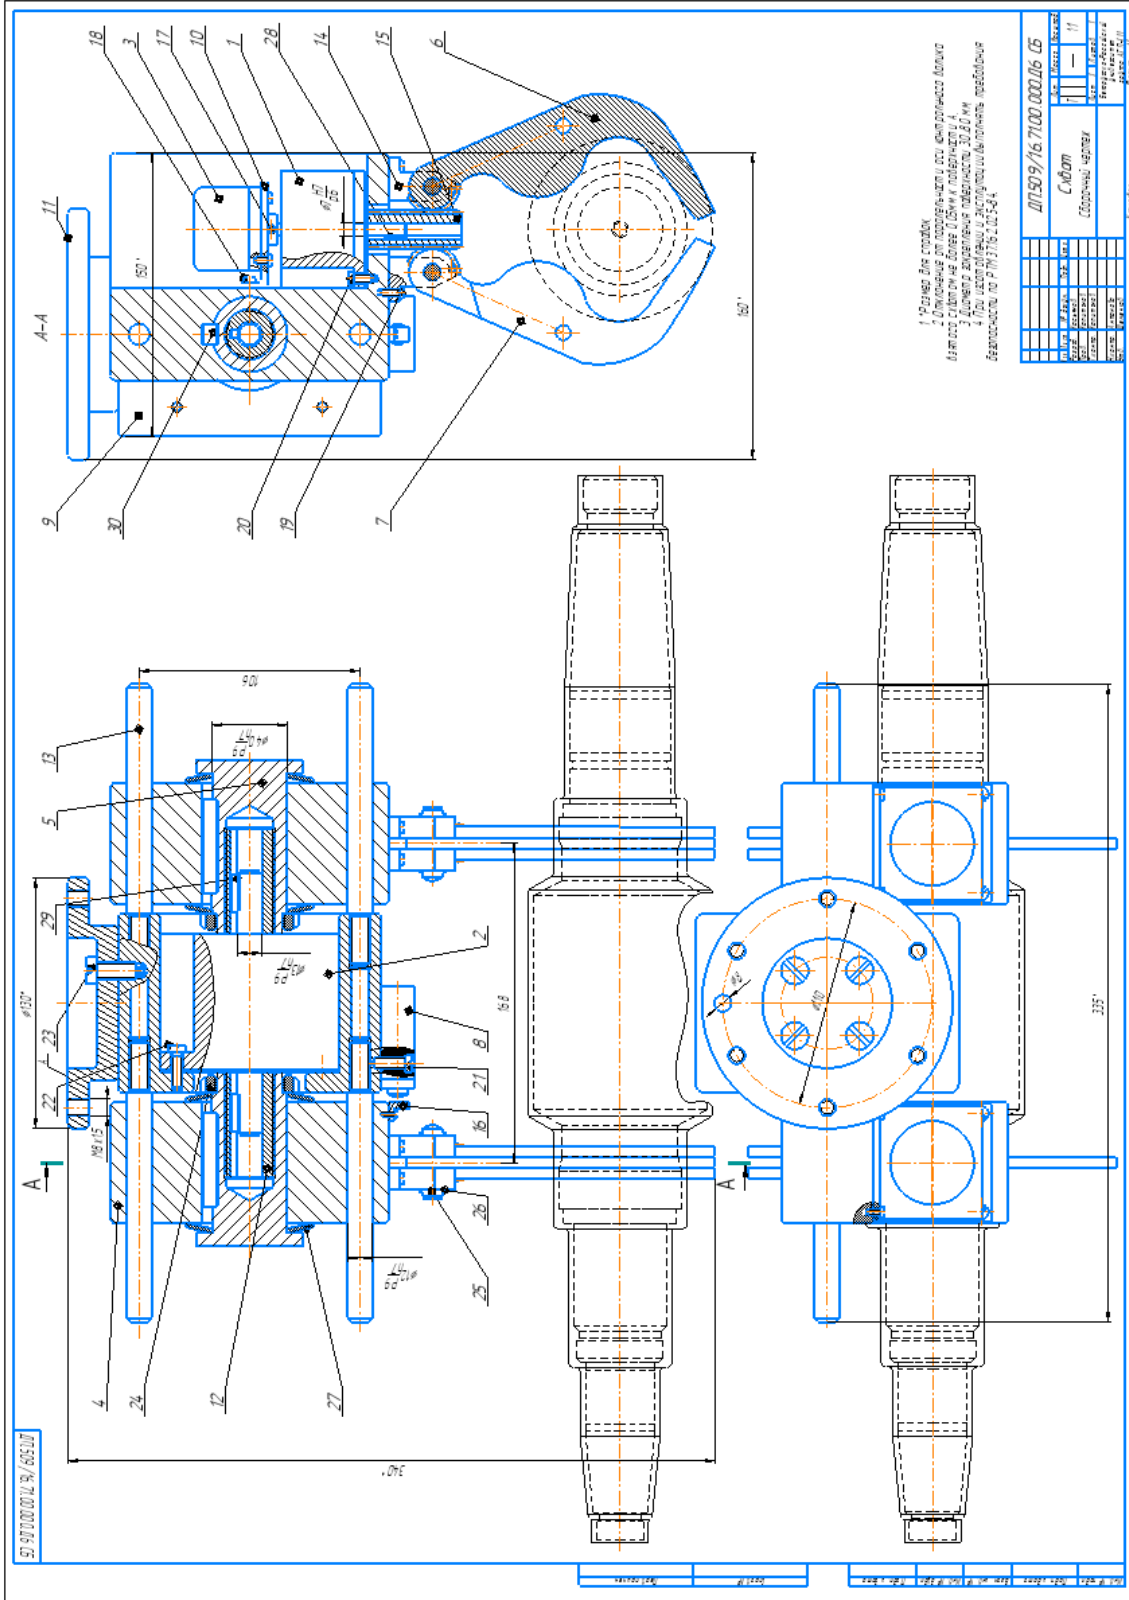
Пример выполнения сборочного чертежа ЗУ (схвата)
